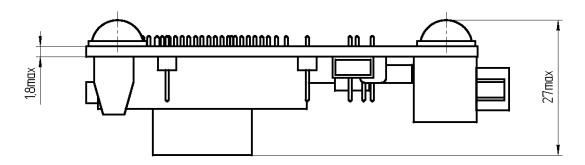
Габаритный чертеж средства отладочного ЦВИЯ.468219.015 Figure B.3 – Outline drawing of evaluation board CVIA.468219.015
